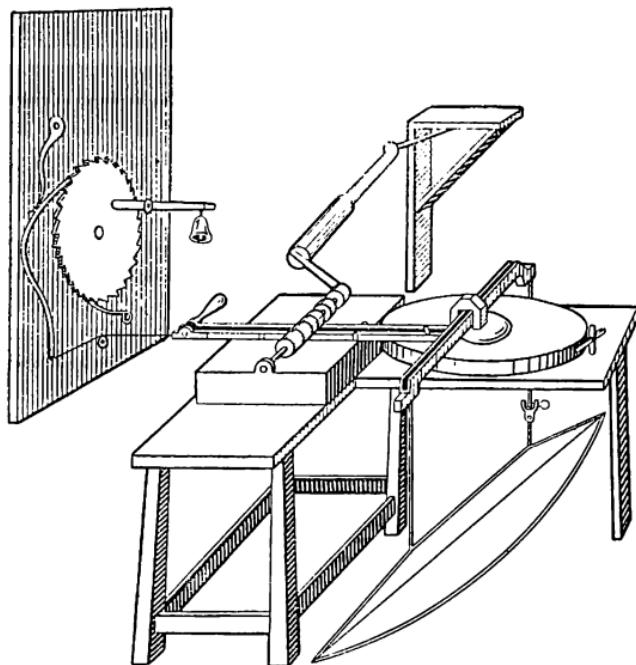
Станки для шлифовки и полировки линз Х. Гюйгенса
